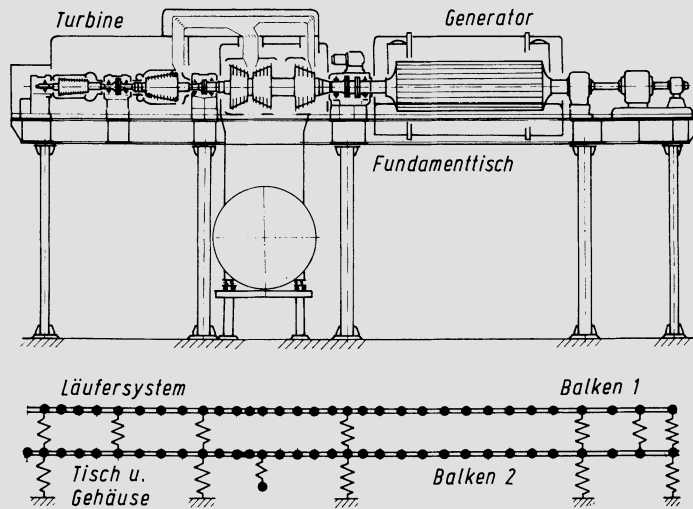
Dampfturbo-Generatorgruppe auf Stahlfundament und zugehöriges Ersatzsystem
